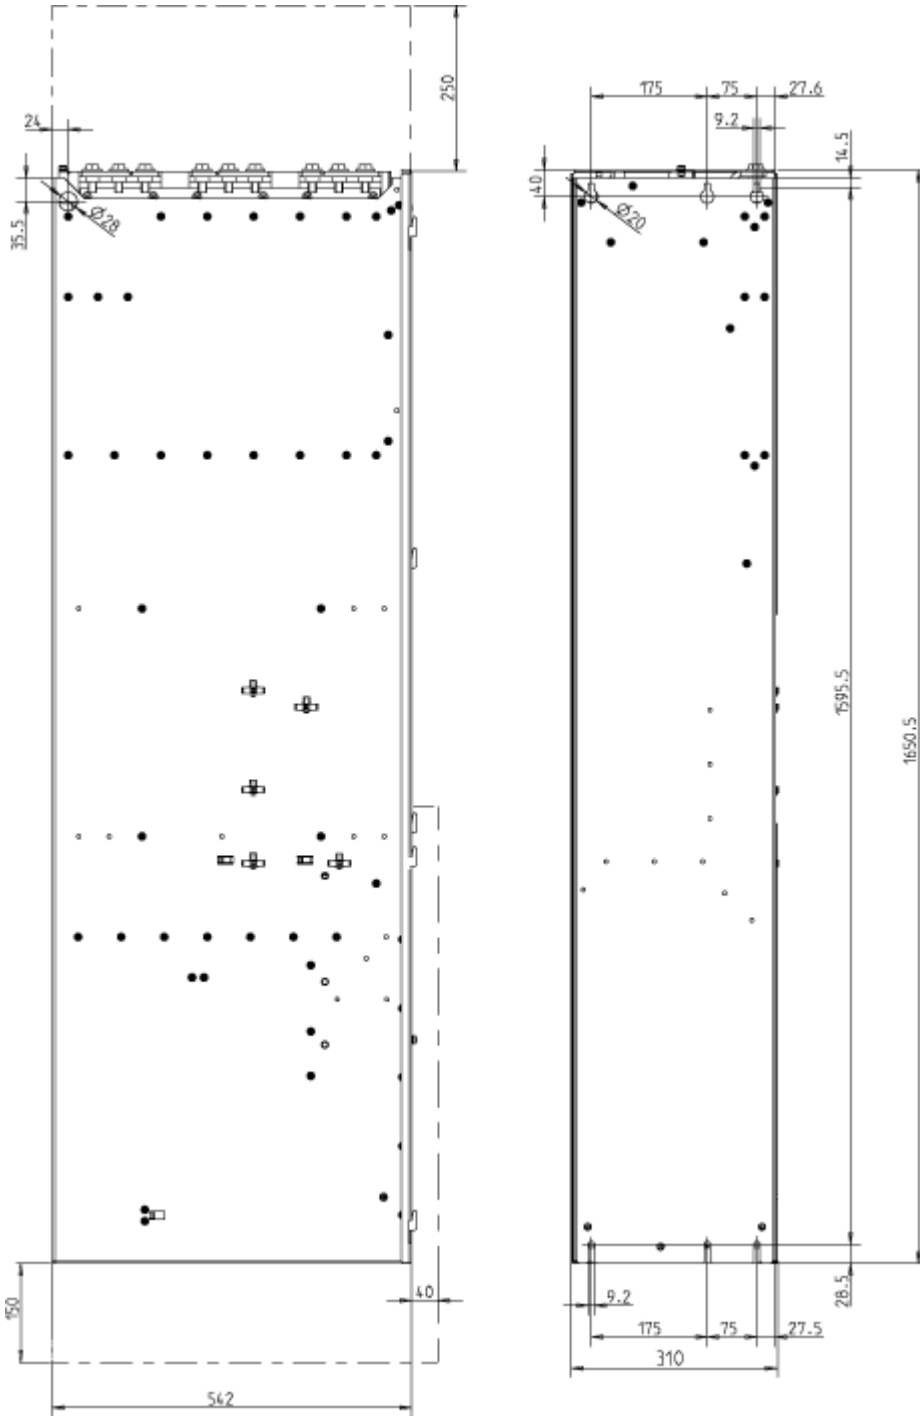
GB、GD 型基本型电源模块的外形尺寸图 侧视图和背视图
